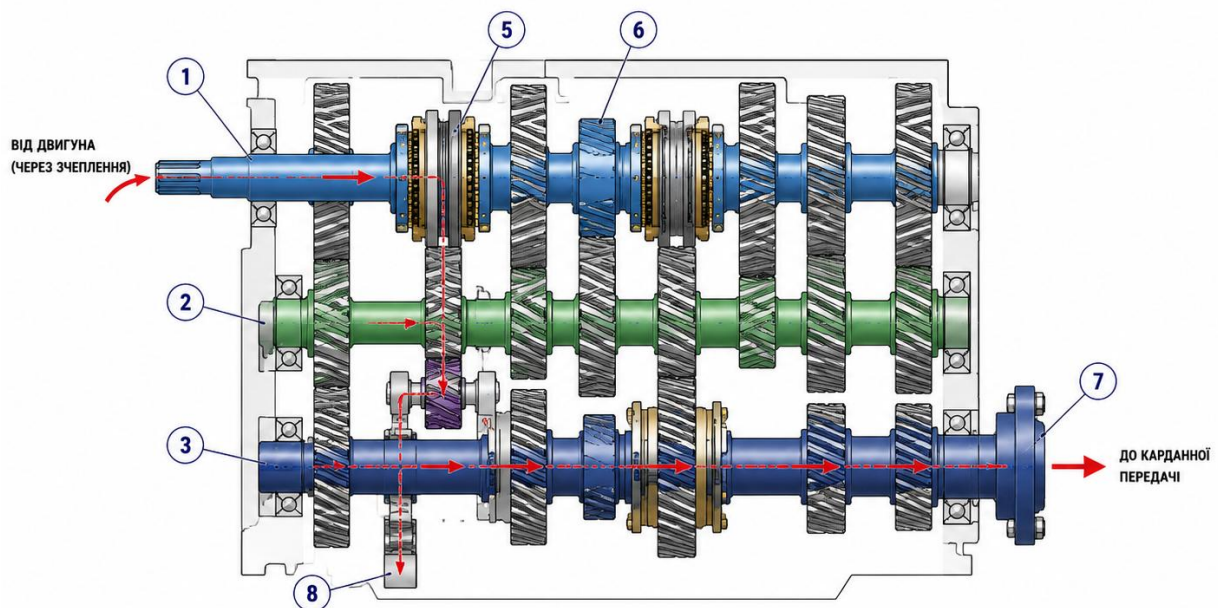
Схема передавання крутного моменту через КПП 2865-6:
